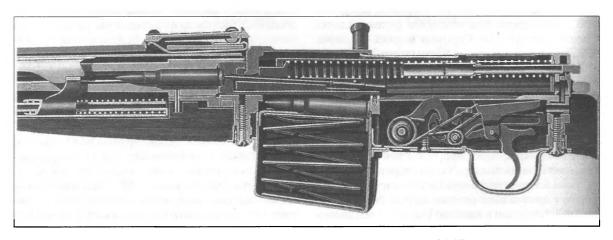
Схема устройства газоотводного двигателя винтовки G.41(W):
